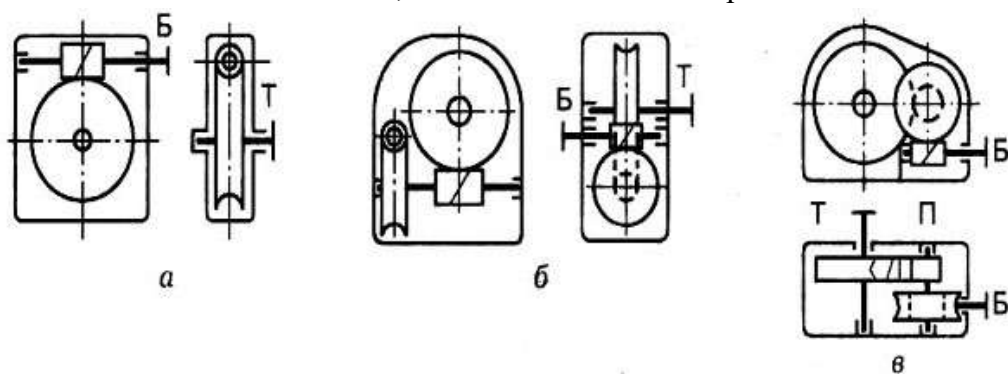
Схемы червячных редукторов: а — одноступенчатый; б — двухступенчатый; в — червячно-цилиндрический
